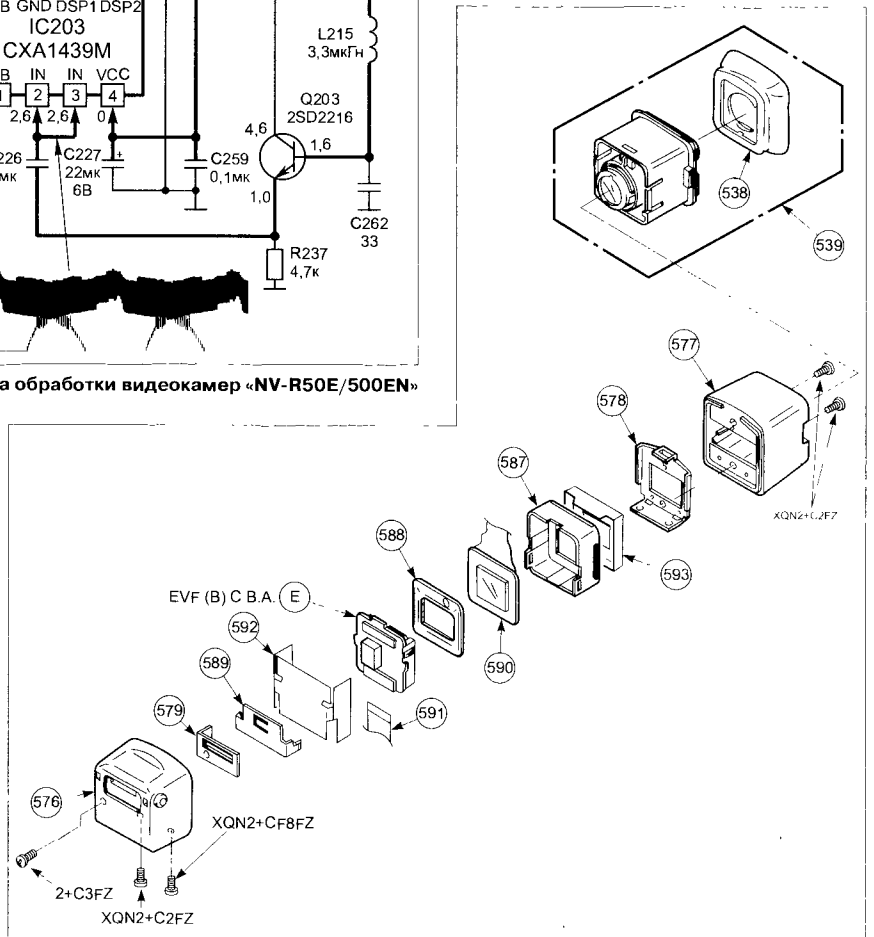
Сборочный чертеж цветного видеоискателя номер «NV-R50E/55E/500E/550EN»
